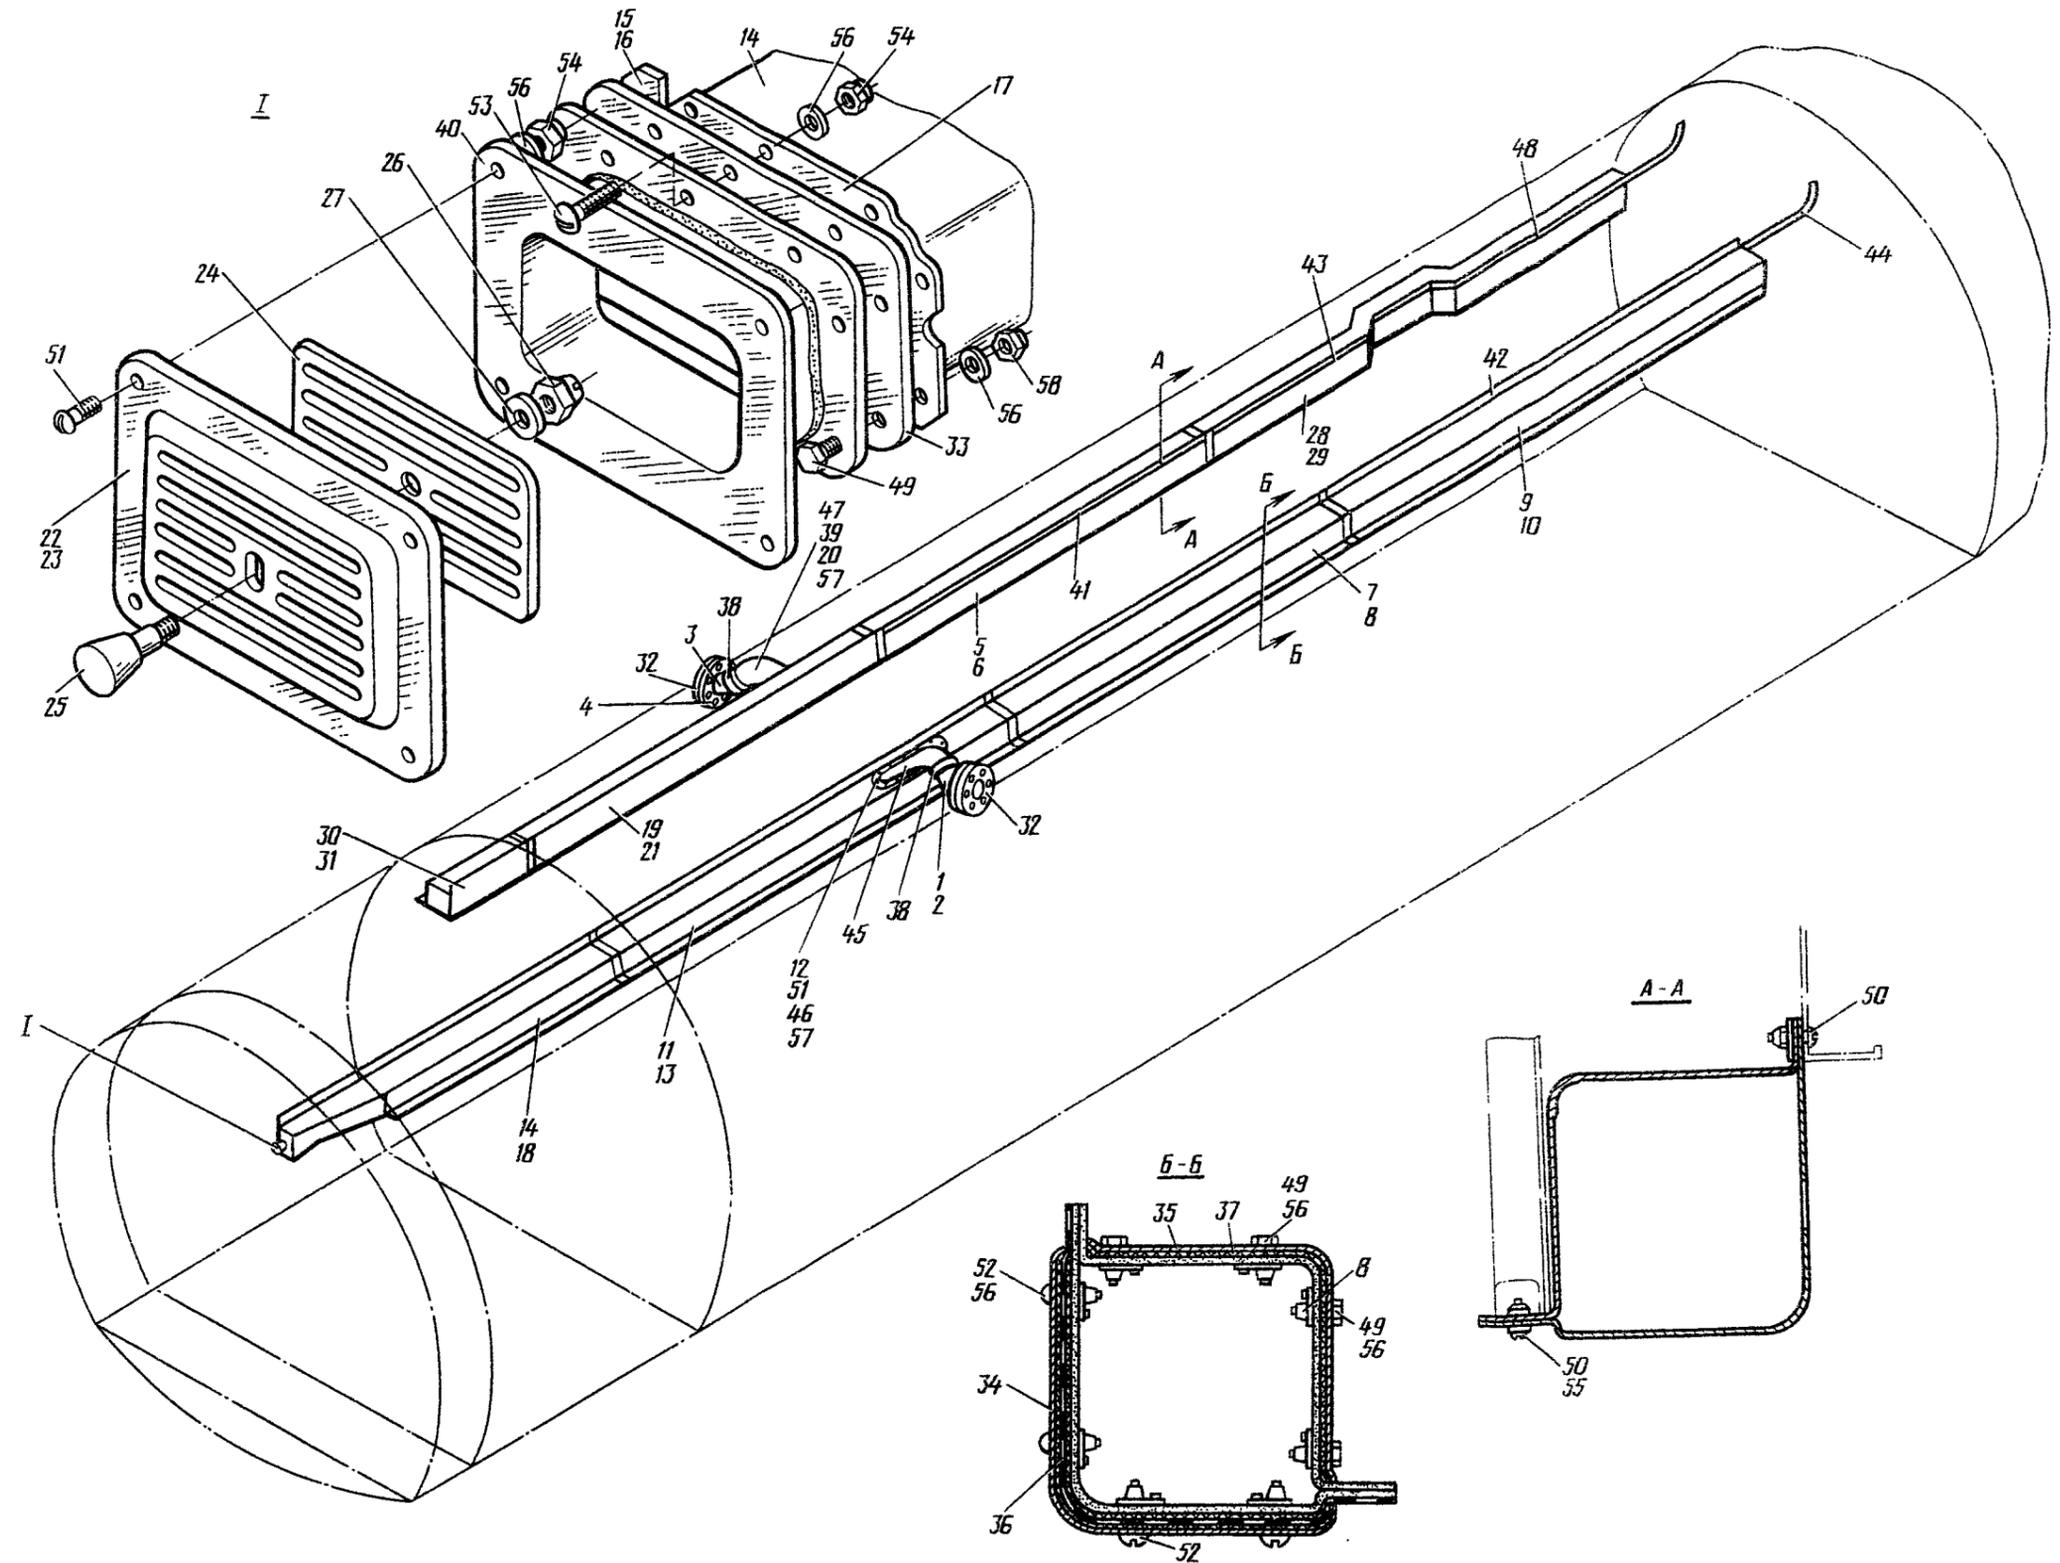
УСТАНОВКА ВЕРХНИХ КОРОБОВ
